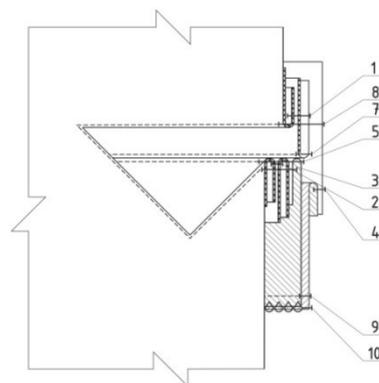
Сборочный чертеж прорезного кармана в рамку с обтачкой сложной формы
